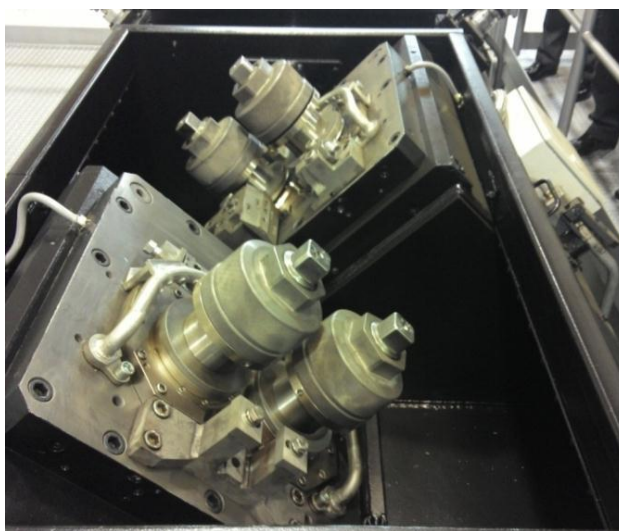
Сдвоенный калибровочный модульный блок ТМВ
